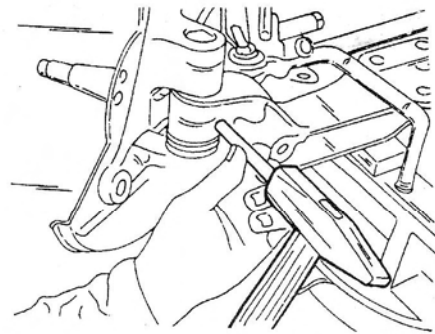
Для снятия поворотного кулака выбить стопорный штифт.
